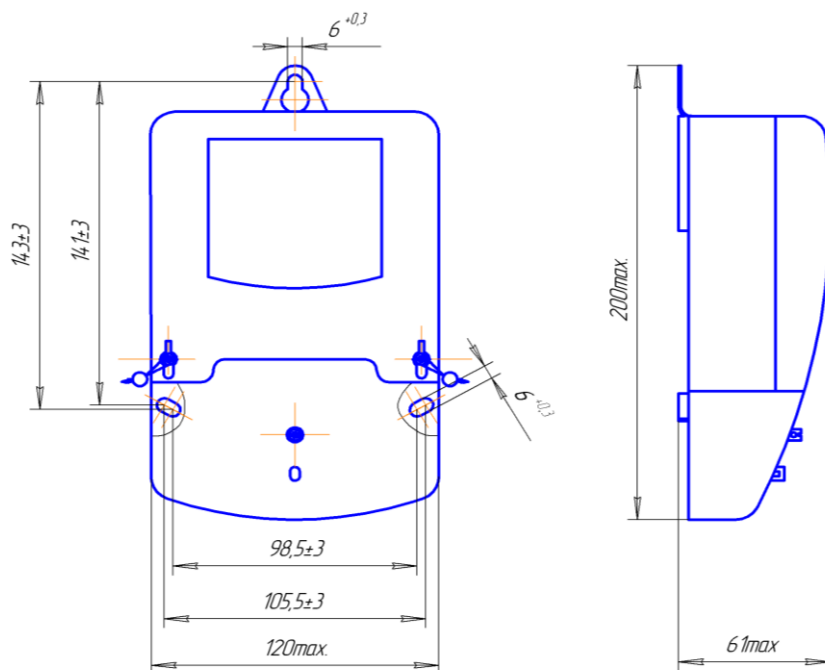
Габаритный чертеж и установочные размеры счетчика (для счетчиков с типом корпуса Н2)
